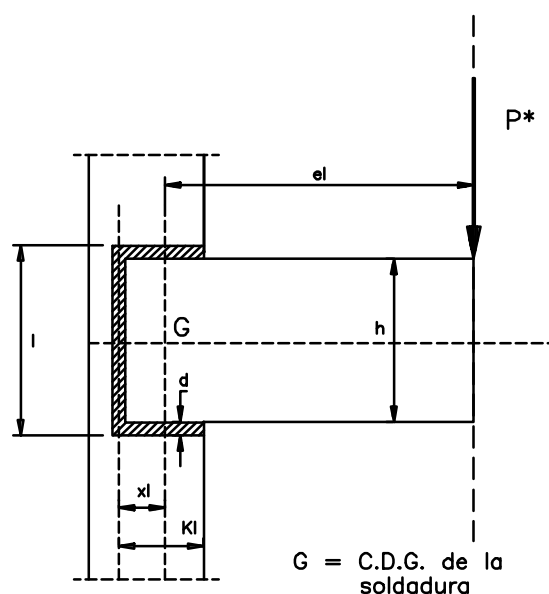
Soldadura en U sometida a torsión en el plano.
